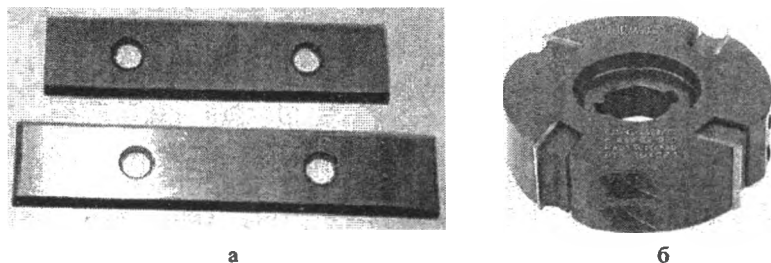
Внешний вид твердосплавного упрочняемого инструмента (а);
